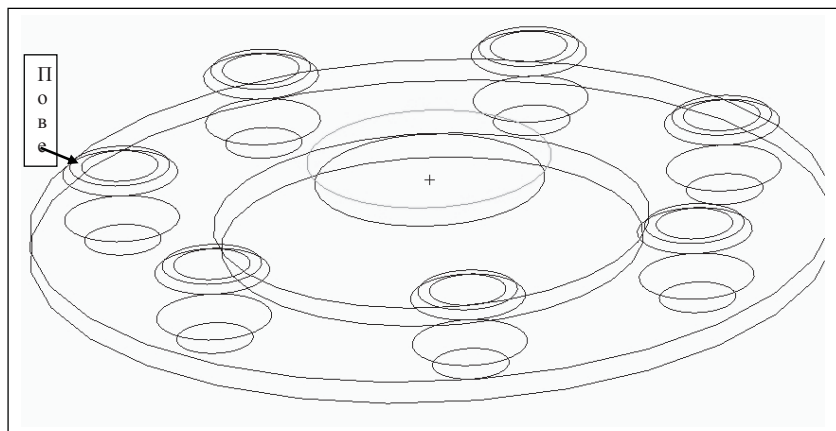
Общий вид зоны конструкции детали для приложения нагрузки
